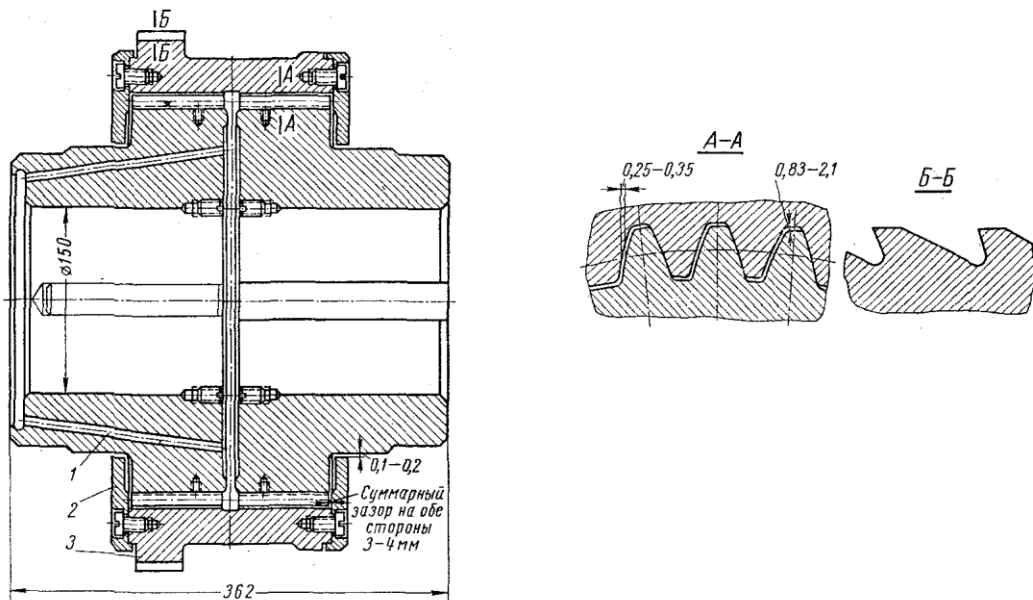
Конструкції зубчатих муфт НЗЛ
